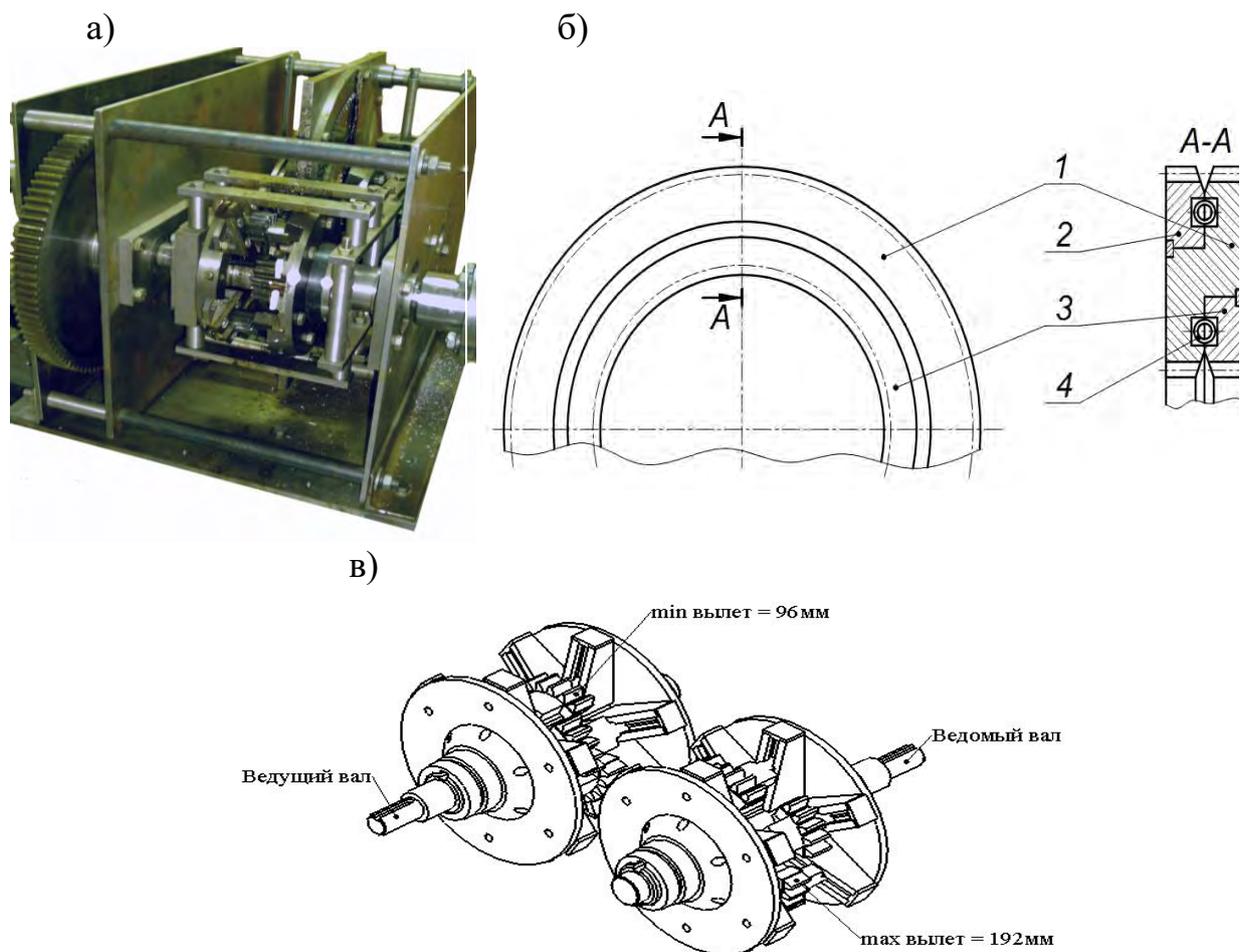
Развернутая зубчатая плавнорегулируемая передача: а – макет передачи; б – центральное зубчатое колесо; в – составные зубчатые колеса
